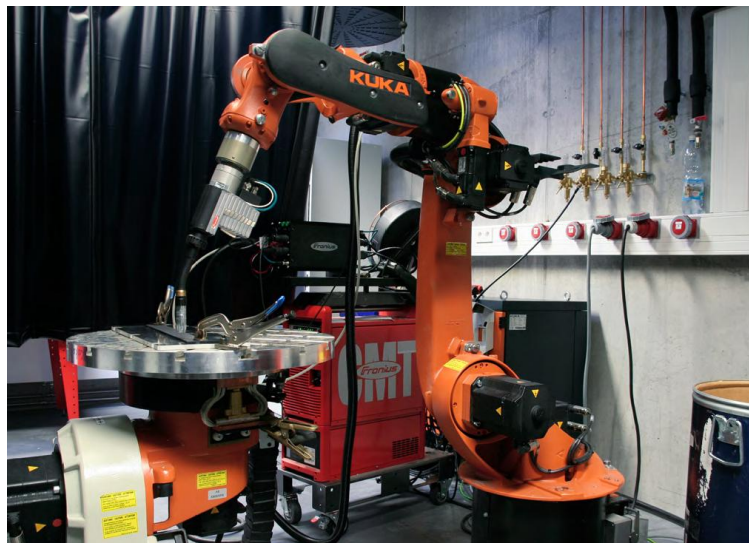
Robot KUKA con equipo de soldadura Fronius (KUKA, 2015)
